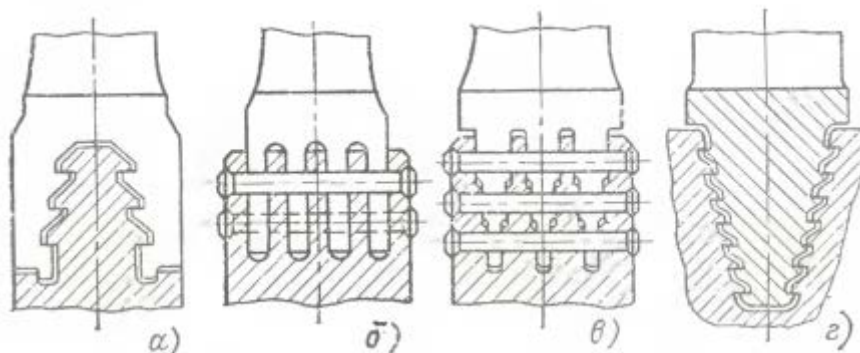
Хвостовики повышенной несущей способности: а – грибовидный трехопорный; б – вильчатый; в – вильчатый равнопрочный; г – елочный с торцевой заводкой.
